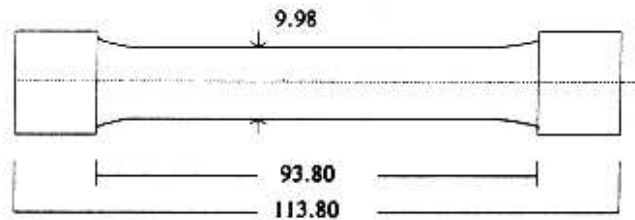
Eprouvette de traction (dimension en mm) [12]
